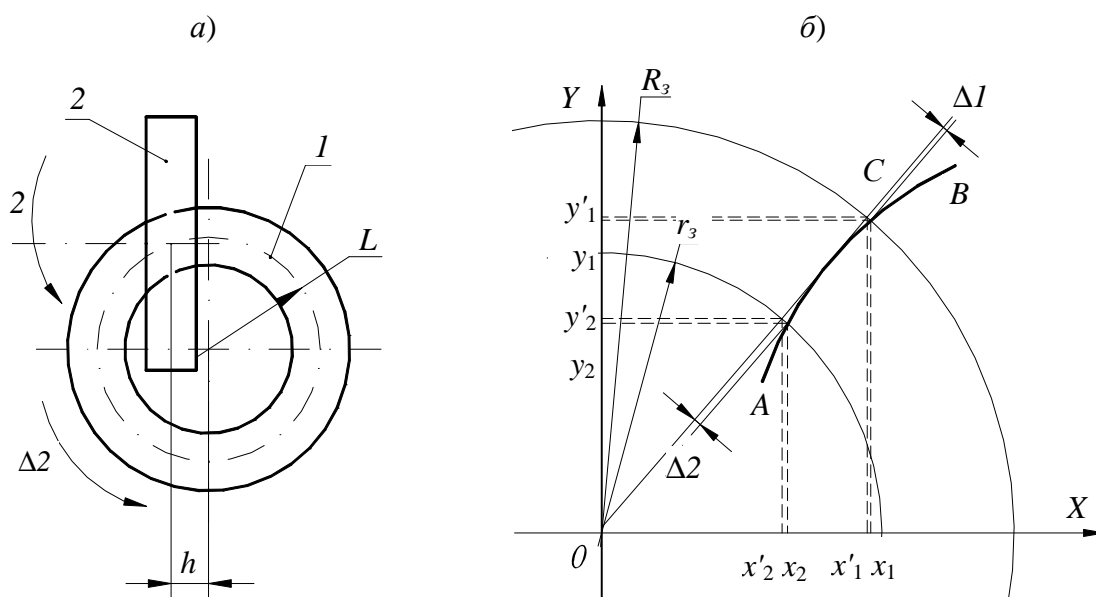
Схема установки (а) резцовой головки при обработке торцового зубчатого контура и траектория ее режущей кромки (б)
